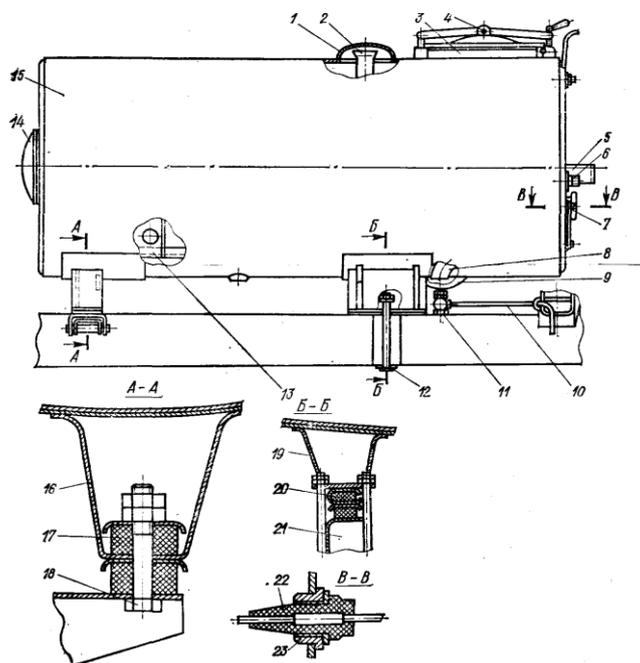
Цистерна: 1, 4 – крышки; 2 – труба контрольная; 3 – горловина; 5 – кронштейн; 6 – труба; 7 – итуцер; 8 – труба заборная; 9 – отстойник; 10 – рычаг; 11 – кран; 12 – стремянка; 13 – волнолом; 14 – крышка горизонтального люка; 15 – обечайка; 16 – опора передняя; 17, 20 – амортизаторы; 18 – болт; 19 – опора задняя; 21 – брус; 22 – гидроконттакт; 23 – итуцер
